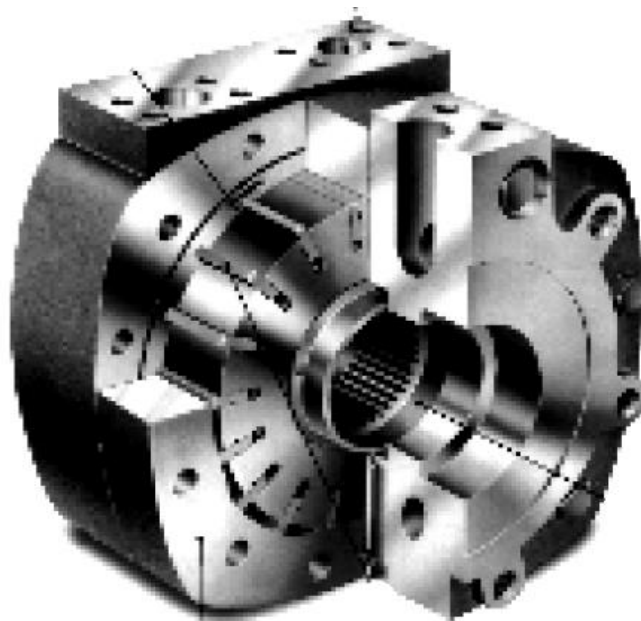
Pompes à palettes à cylindrée fixe [8]
